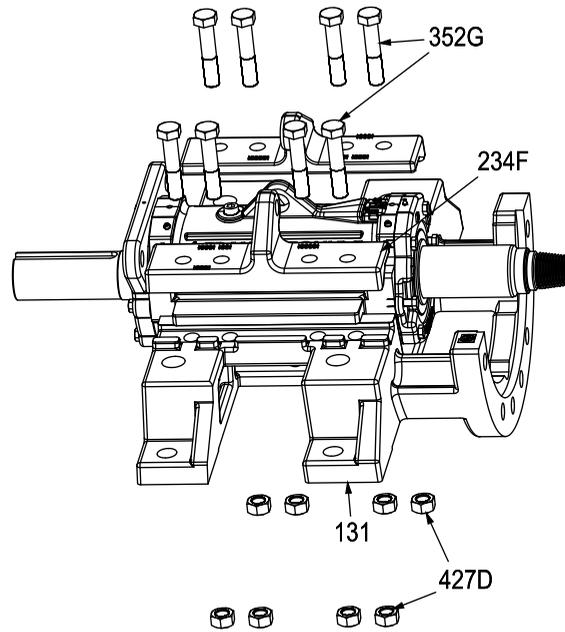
Dépose de la plaque de réglage du cadre de roulement
